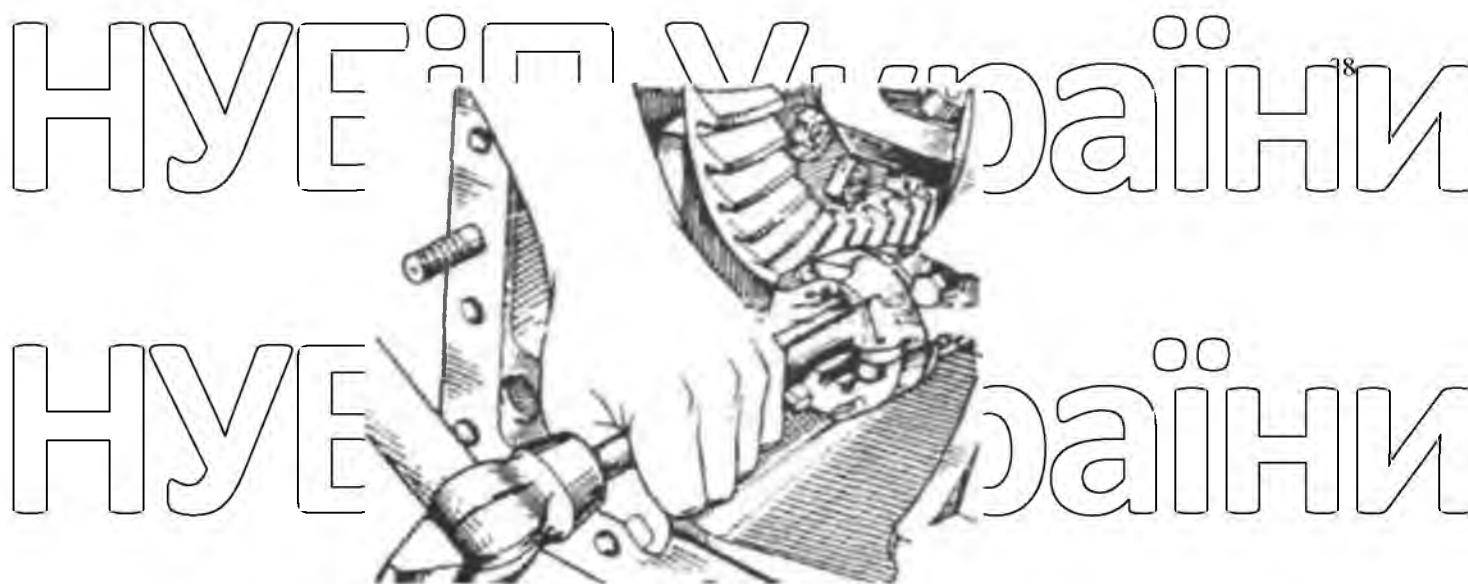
Вибивання вала коронної шестерні в зборі з шестернею,
